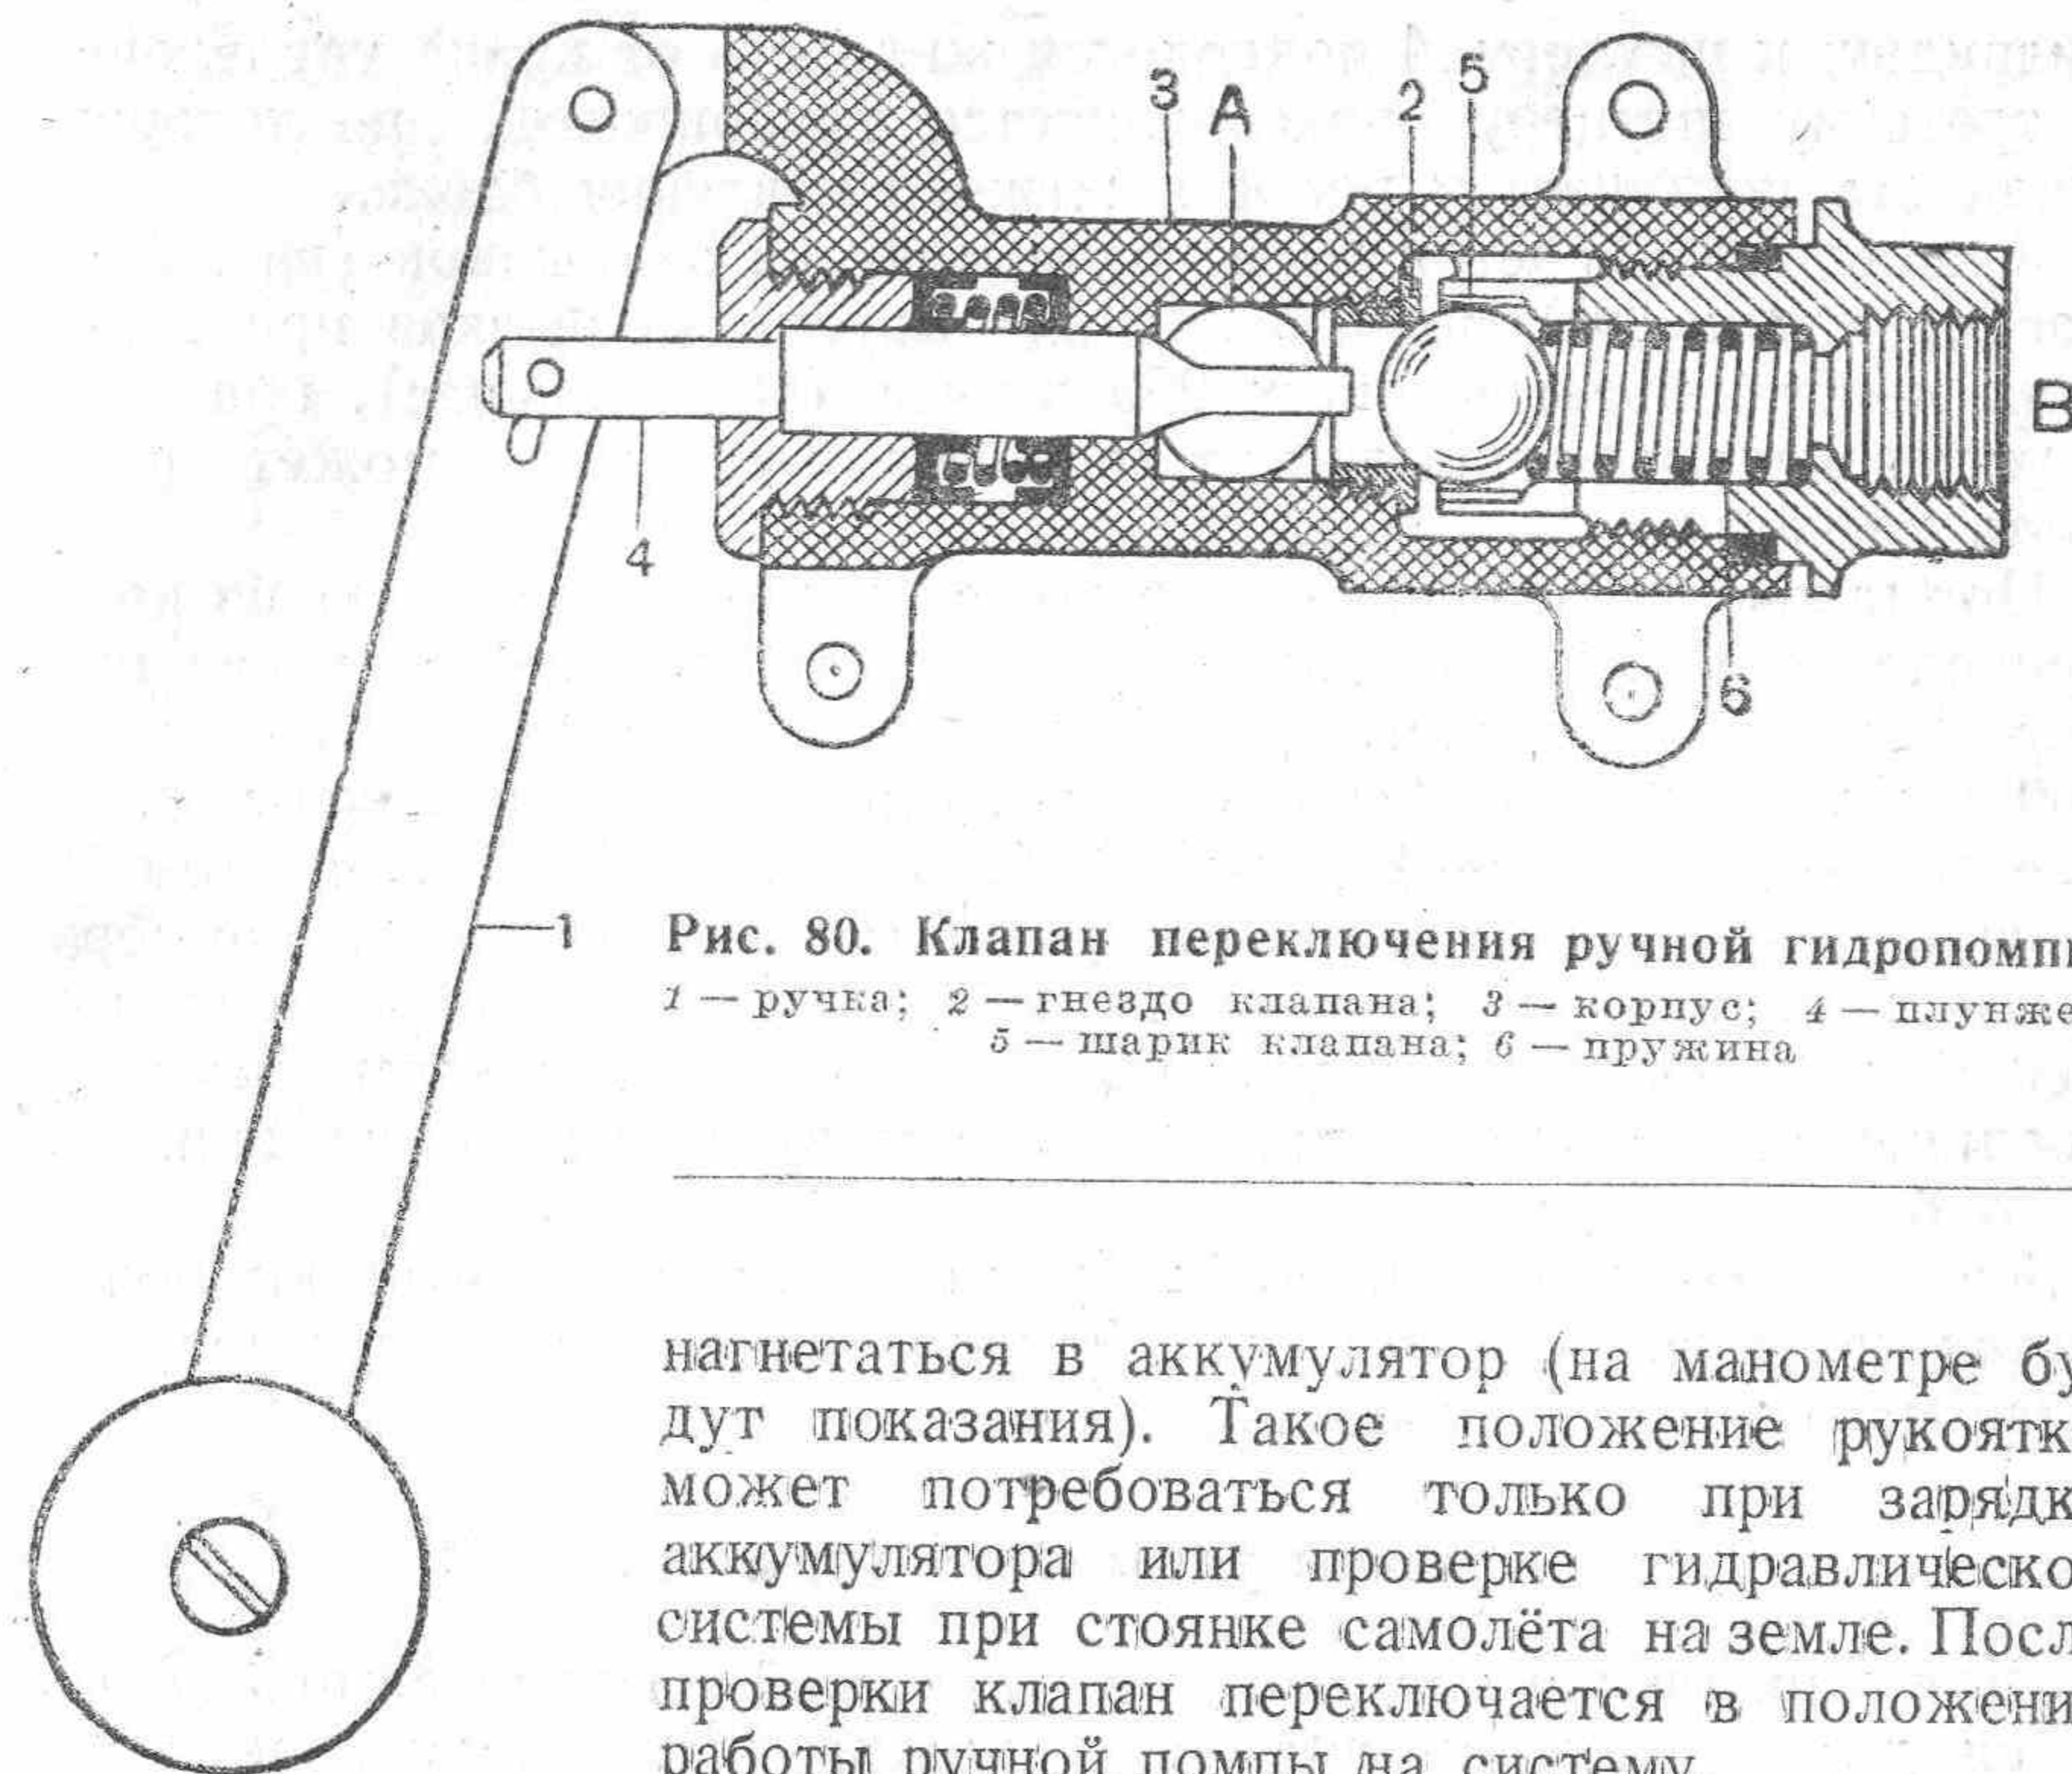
Клапан переключения ручной гидropомпы: 1 — ручка; 2 — гнездо клапана; 3 — корпус; 4 — плунжер; 5 — шарик клапана; 6 — пружина
